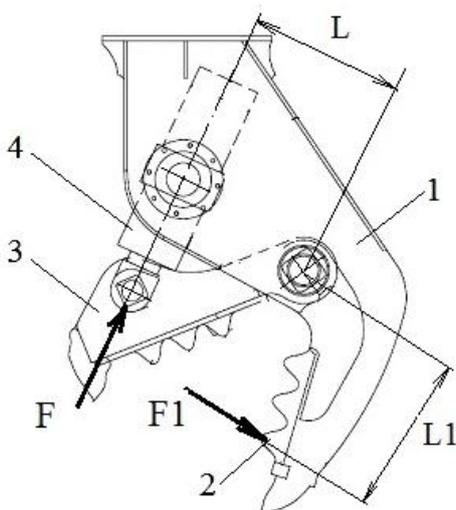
Расчетная схема определения силы разрушения бетона:
